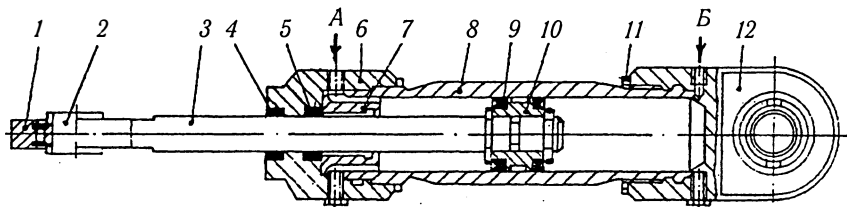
Цилиндр поршневой ГРМ (в сборе): 1 — головка поршневого штока, 2 — сферический подшипник, 3 — поршневой шток, 4 — грязесъемное кольцо, 5 — уплотнительная манжета из маслостойкого материала, 6 — передняя крышка, 7 — направляющая втулка, 8 — цилиндровая втулка, 9 — уплотнительная манжета из маслостойкого материала, 10 — поршень, 11 — контргайка, 12 — задняя крышка, А и Б — подача рабочей жидкости
